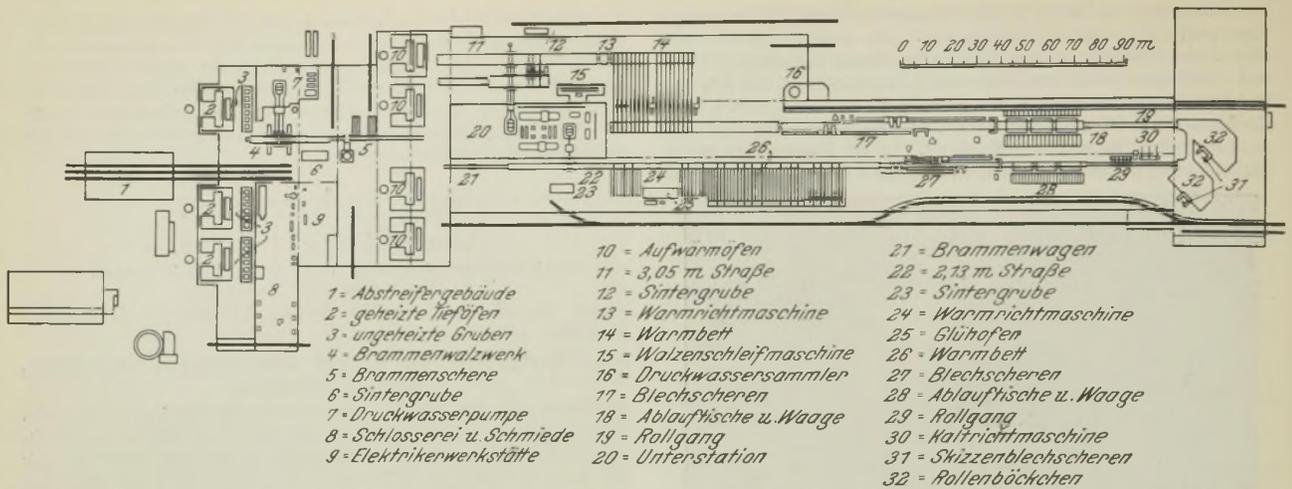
Grundriß der Blechwalzwerksanlage.
